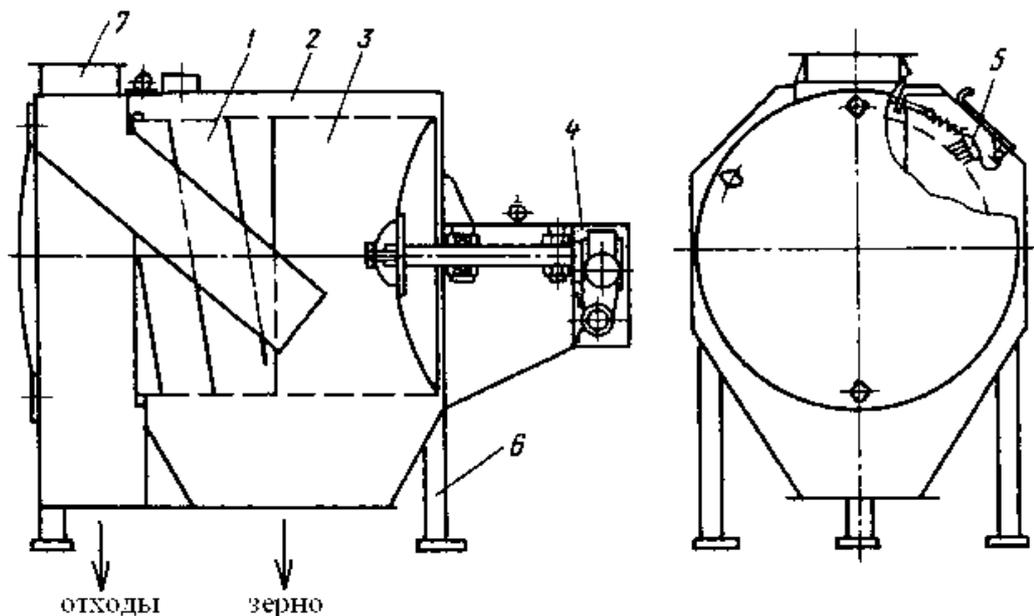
Барабанный скальператор А1-Б30: 1 – приемное устройство; 2 – корпус; 3 – ситовой барабан; 4 – привод; 5 – щетка-очиститель; 6 – стойка; 7 – приемный патрубок
